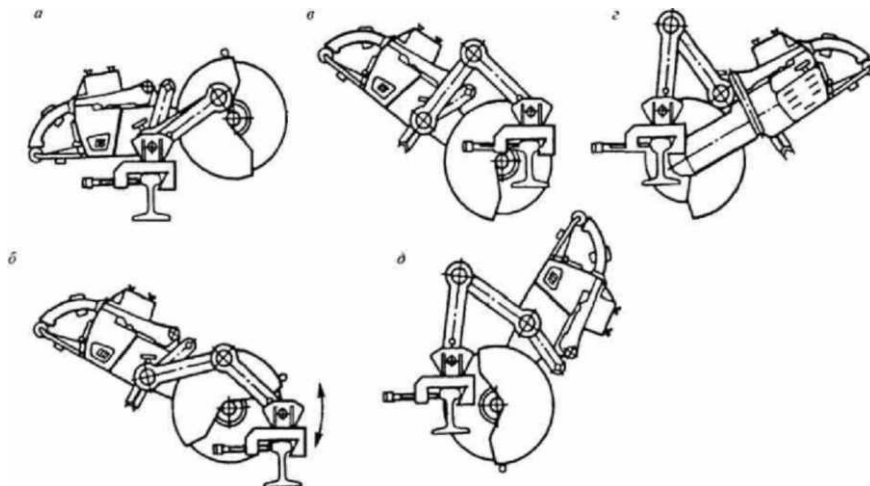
Изменение положений частей станка РР 80 при резании рельса
